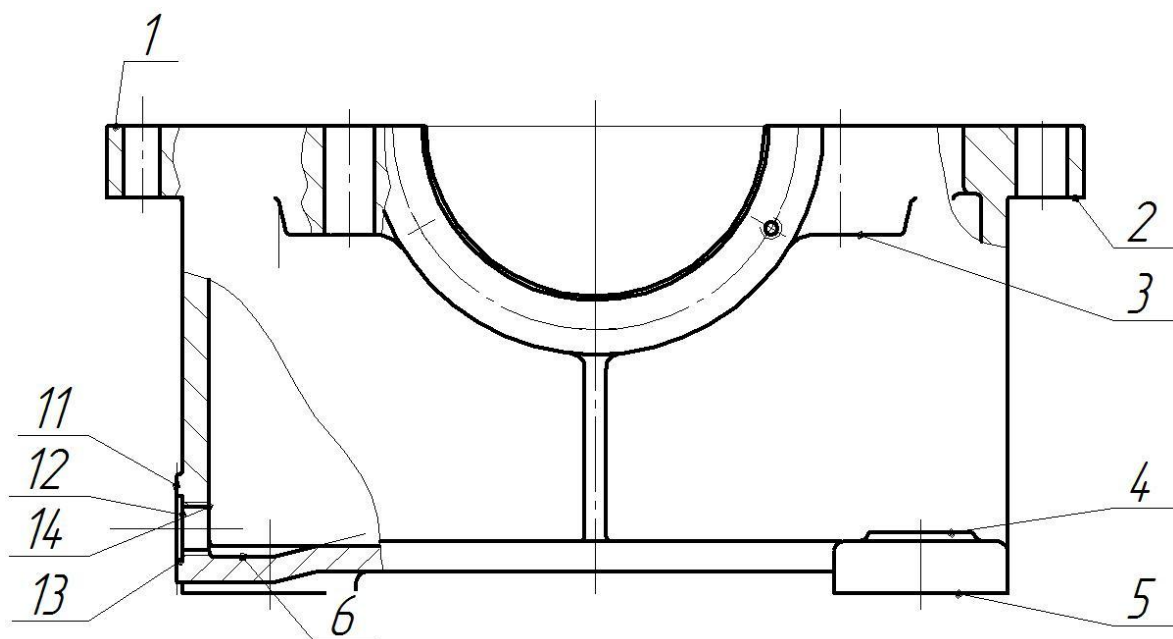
Эскиз корпуса червячного редуктора
